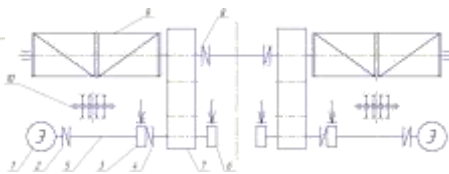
Конструкция с «двойным» редуктором и линейным расположением барабанов (схема №3)
